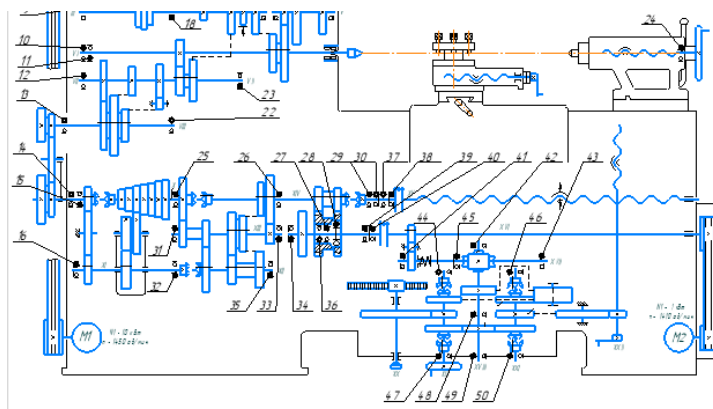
Кинематическая схема привода подач токарно-винторезного станка 16K20
